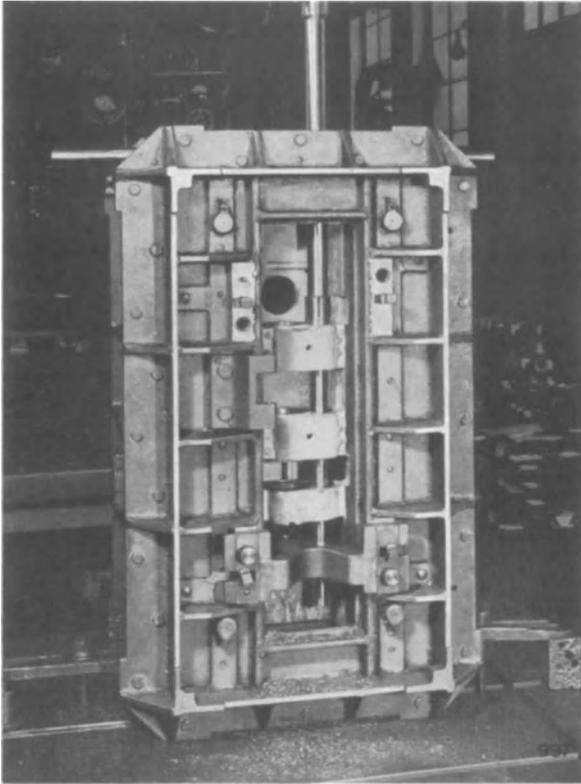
Doppelt geführte Bohrstange beim Bohren des Unterschlittens einer Fräsmaschine
